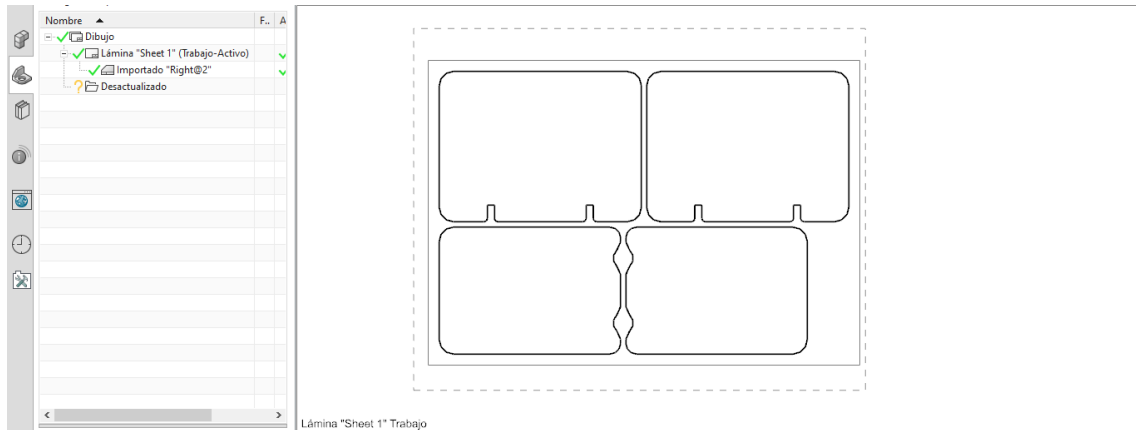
Plano de corte de ejemplo para piezas en acetato / Fuente: Propia
